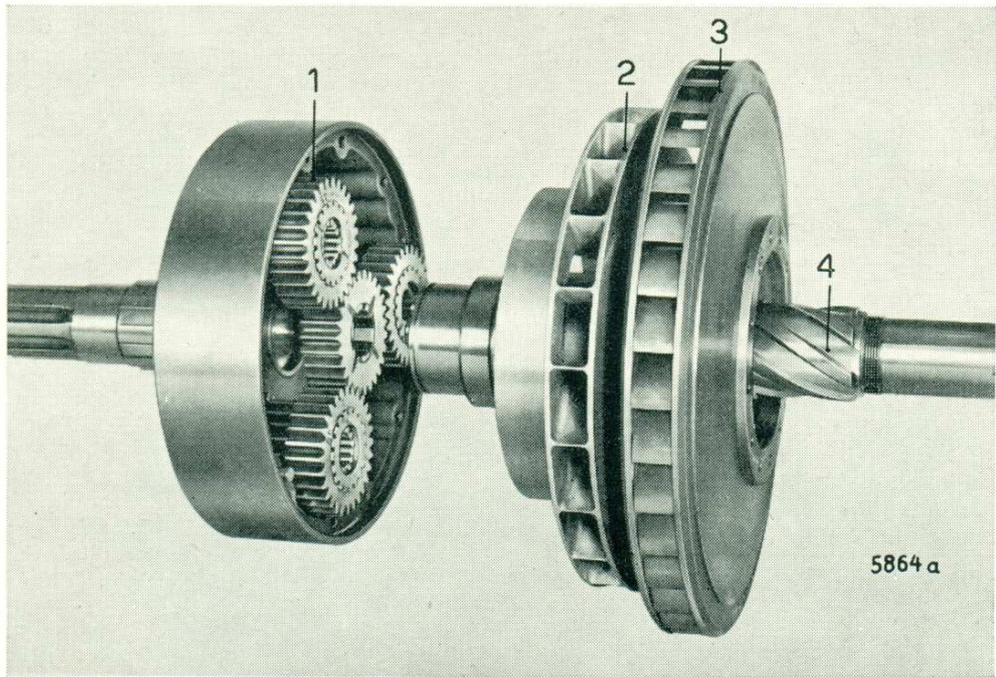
Verteilergetriebe mit Pumpen- und Turbinenrad
